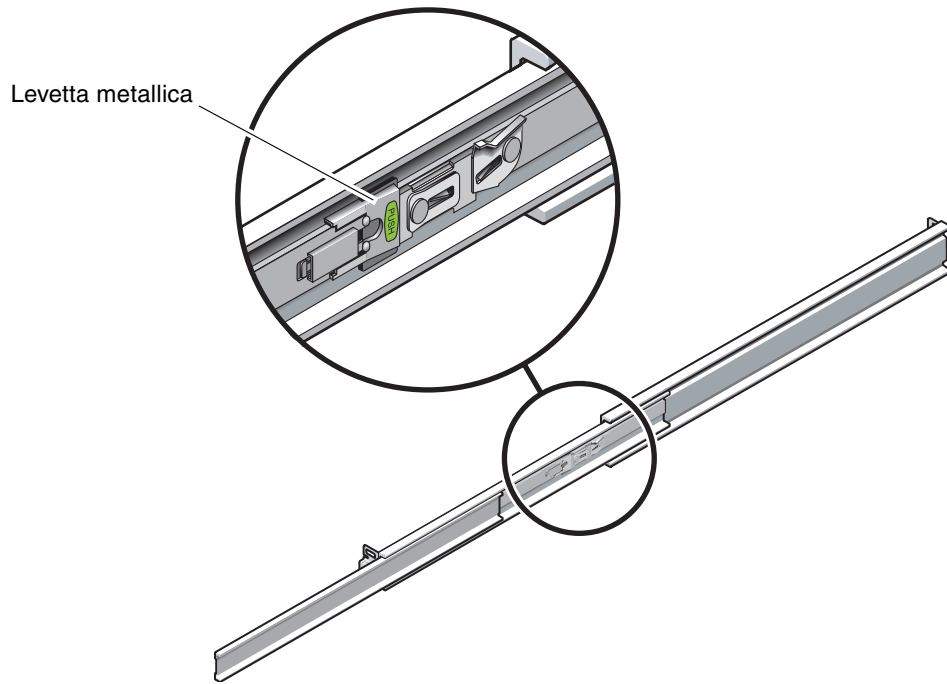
Sblocco della sezione centrale dalla guida
